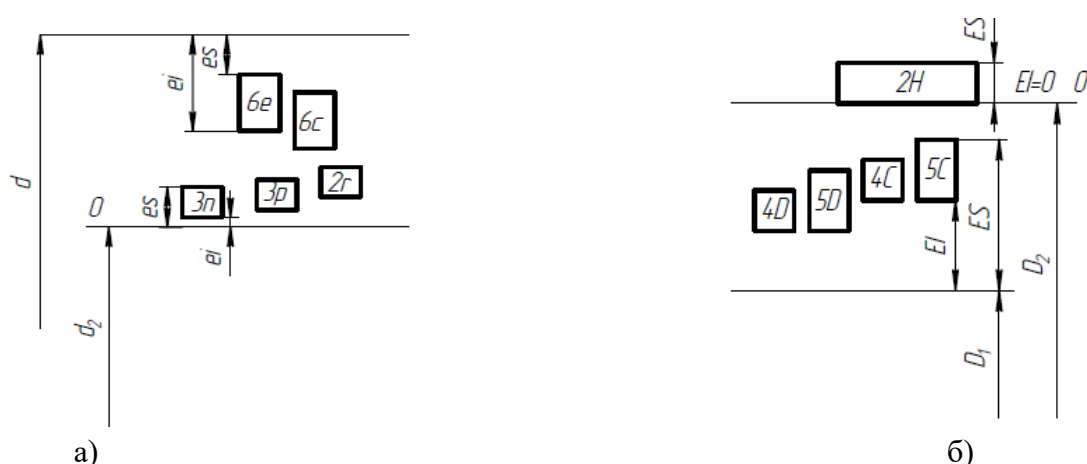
Основные отклонения метрической резьбы при посадке с натягом: а) наружная резьба; б) внутренняя резьба
